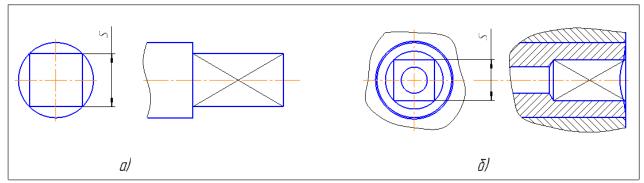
Выступы и отверстия под ключ: а – квадратные выступы; б – квадратные отверстия
